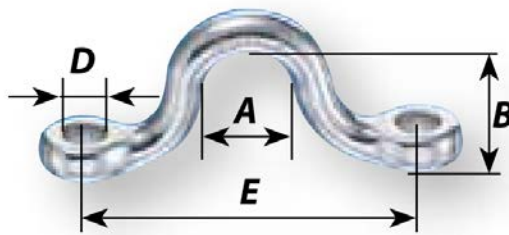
SADDLE E DIMENSIONI COMPONENTE
